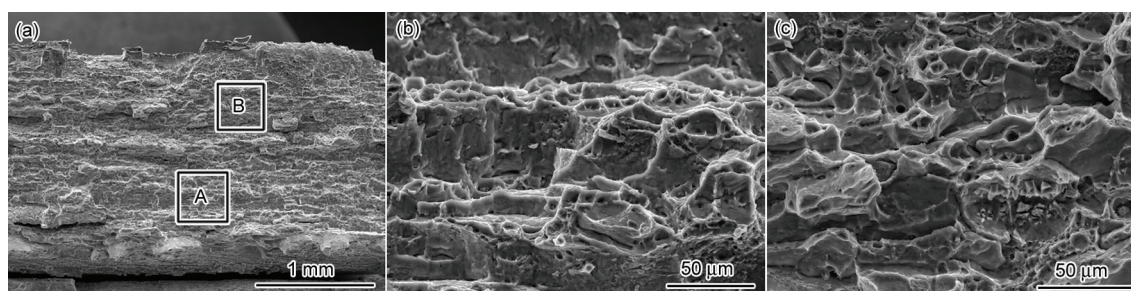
转速 800 r/min, 搅拌针长 2.5 mm 工艺条件下 2099-T83/2060-T8 Al-Li 合金 FSW 搭接接头剥离试样断口形貌
